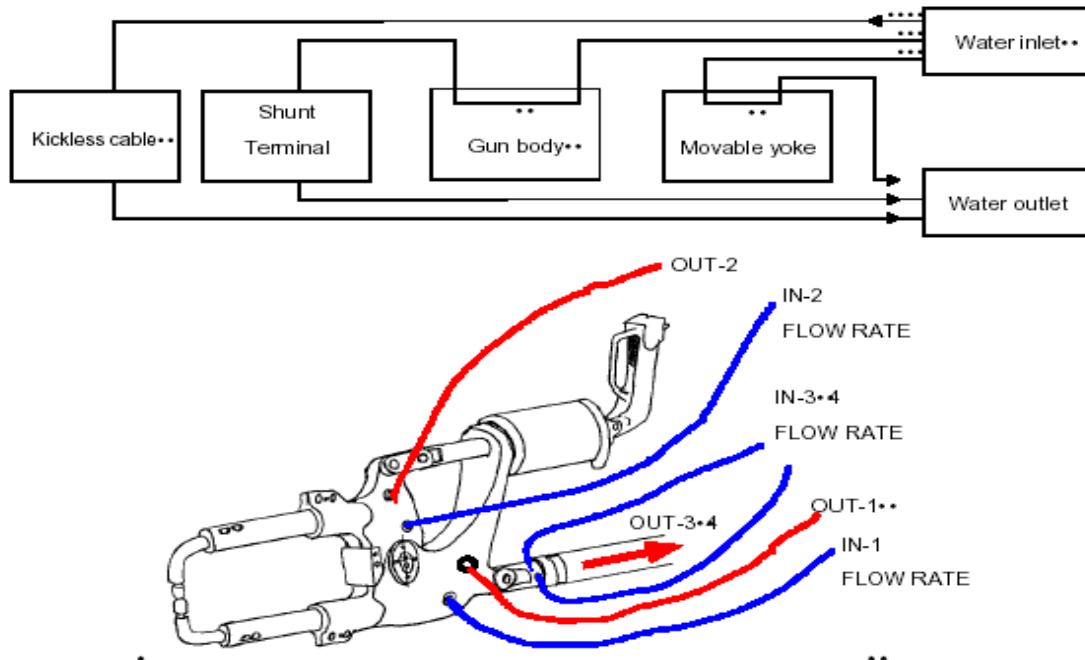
Estándar para una soldadora tipo X.
